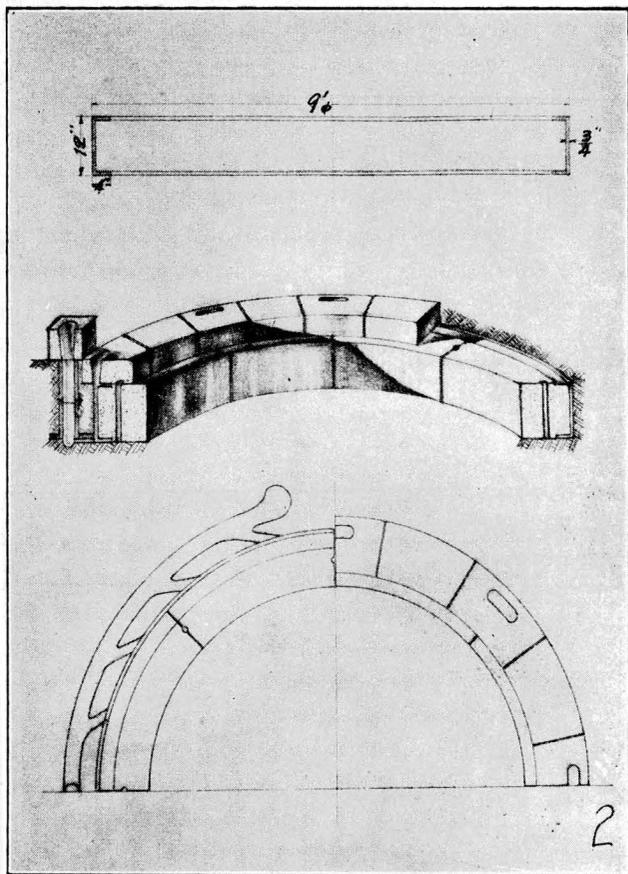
Detalhes do molde de anel para obóbada de forno elétrico
